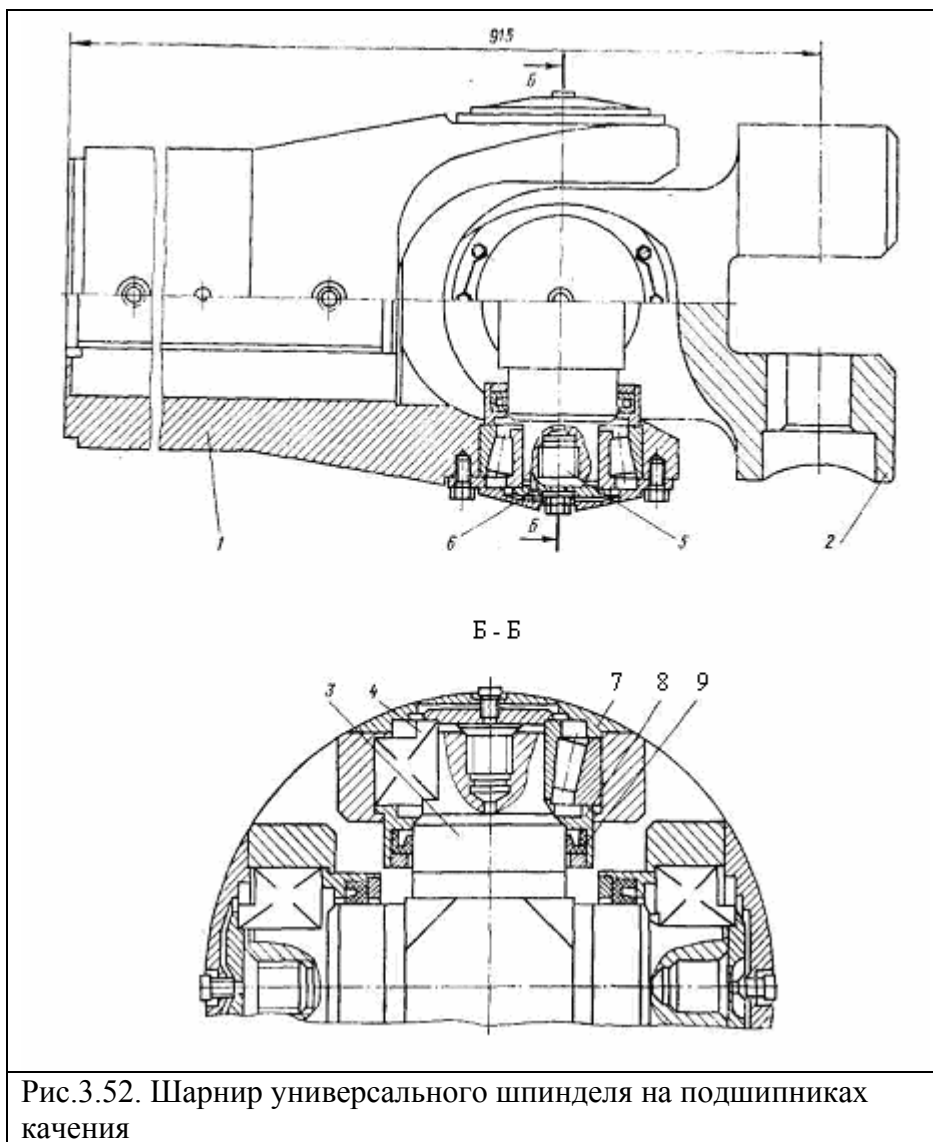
Шарнир универсального шпинделя на подшипниках качения
